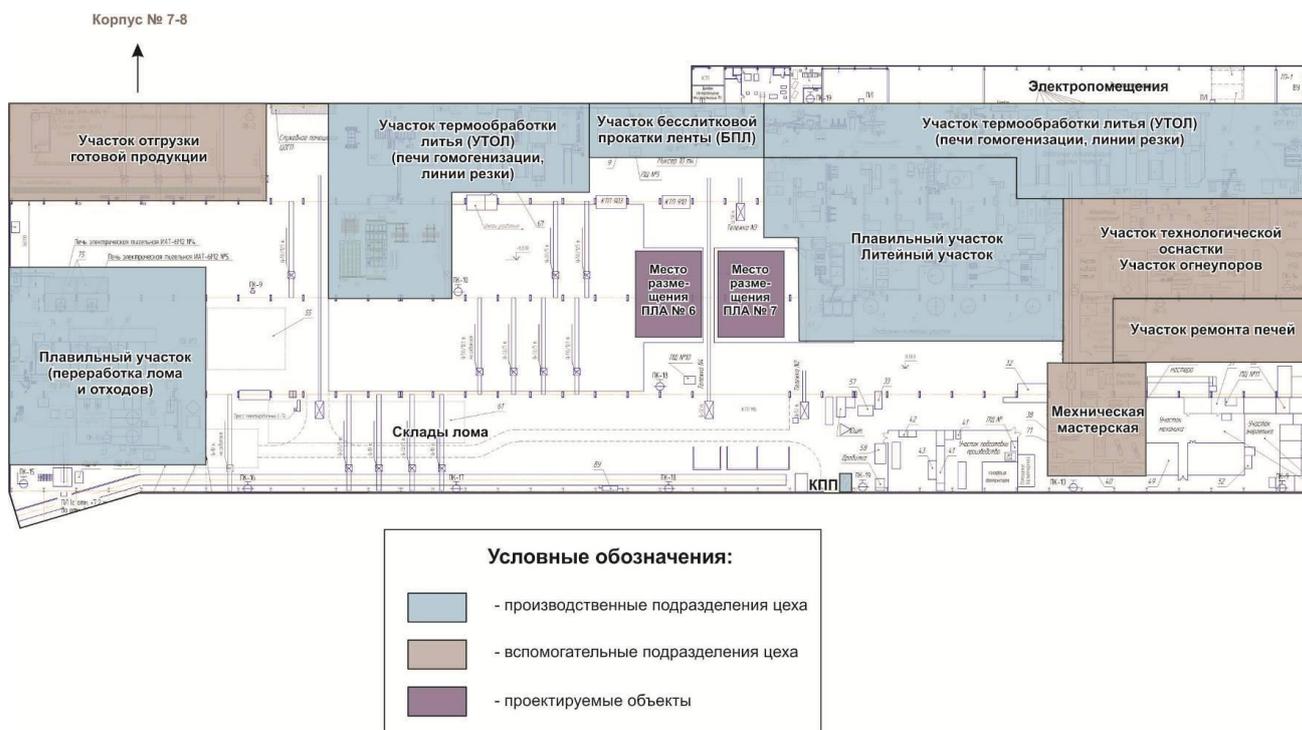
Схема плавильного цеха (корпус № 9)
